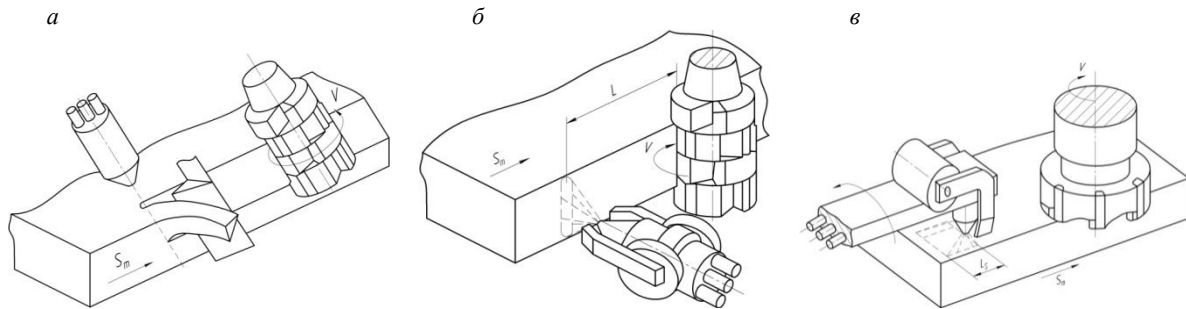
Різновиди схем плазмово-механічного фрезерування: S_m – хвилинна подача; V – швидкість обертання фрези; L – відстань між фрезою та плазмотроном; L_s – довжина опорної плями нагрівання
